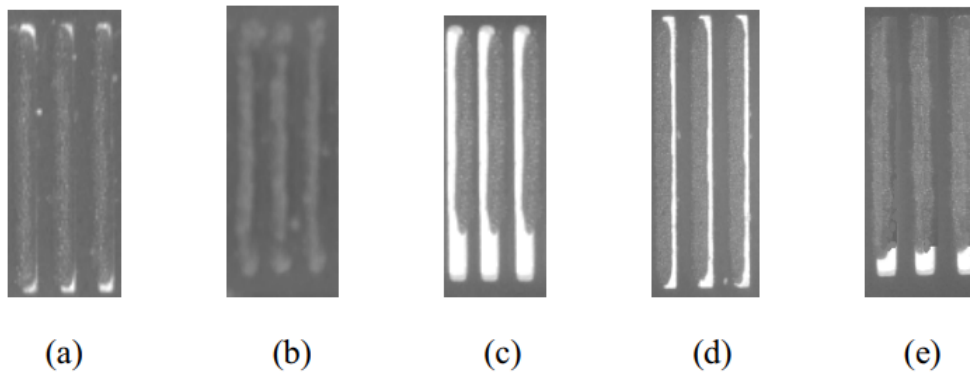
Defeitos de deposição de solda[10]: (a) bom; (b) excesso; (c) insuficiente; (d) deslocação horizontal; (e) deslocação vertical.
